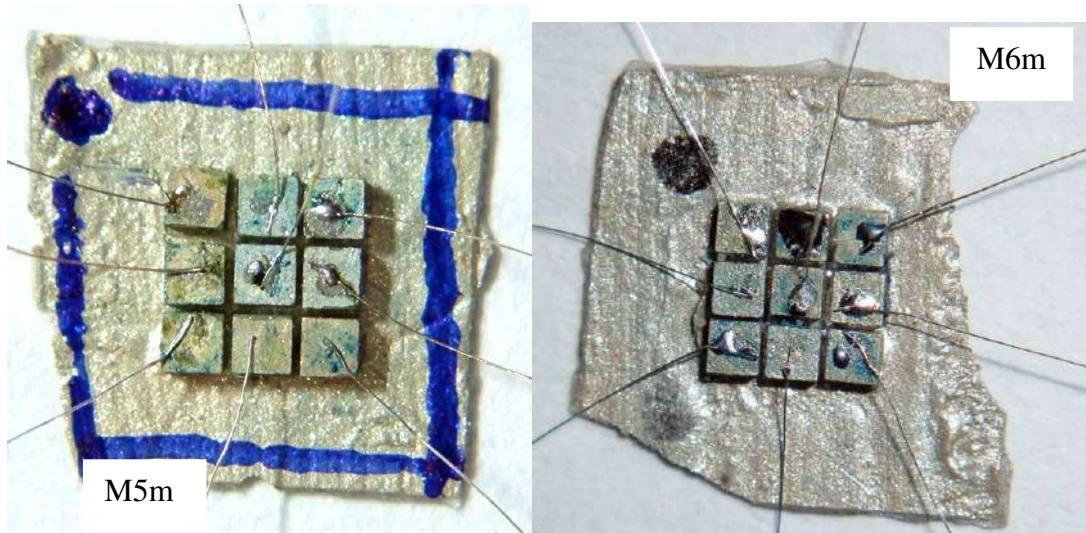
Matrizes M5m e M6m (montadas elemento a elemento) com pouquíssima solda nos contatos. O elemento M5m11 deslocou-se durante a soldagem do fio, apesar de ter-se aquecido o mínimo possível para a operação de soldar. O mesmo não ocorreu com a matriz M6m. Todos os elementos das duas matrizes receberam aproximadamente a mesma quantidade de calor.
